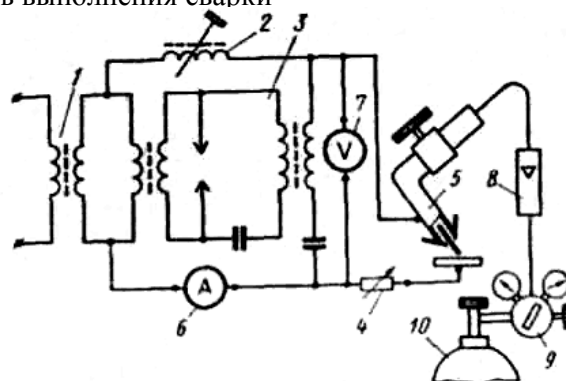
Схема установки для аргоно-дуговой электрической сварки неплавящимся вольфрамовым электродом на переменном токе: 1 — сварочный трансформатор; 2 — индуктивный регулятор сварочного тока; 3 — осциллятор; 4 — балластный реостат; 5 — газозлектрическая горелка; 6 — амперметр; 7 — вольтметр; 8 — расходомер газа; 9 — редуктор; 10 — баллон с газом
